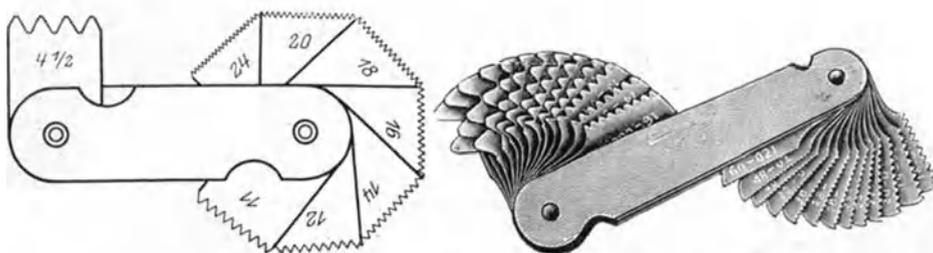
u. 166. Gewindeflanschen für Außen- und Innengewinde.
